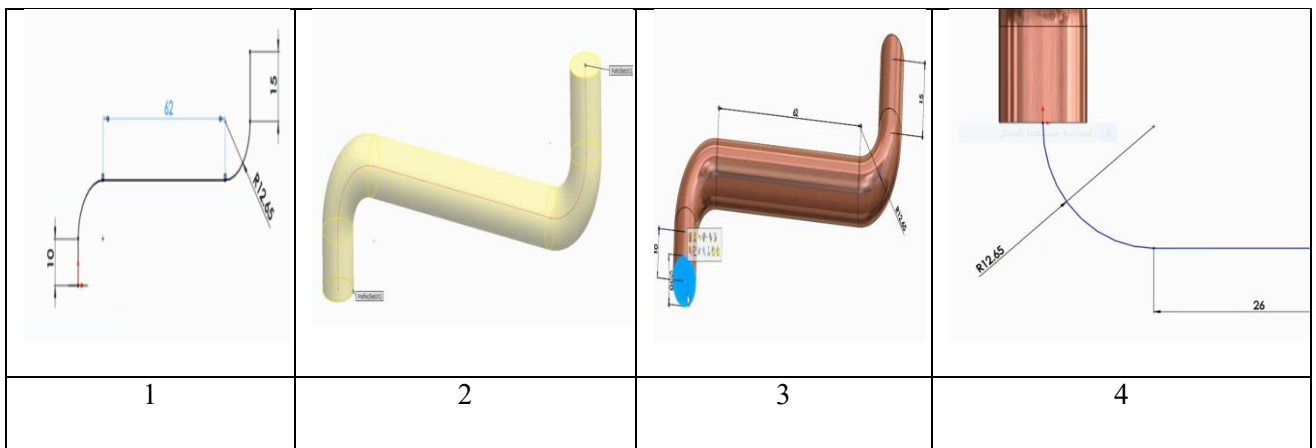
Les étapes de conception et de dimensionnement de la forme du premier tube.
